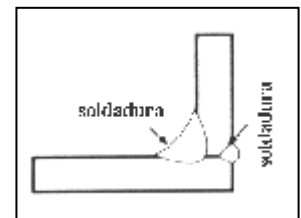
Esquina soldada desde ambos lados - pobre adentro, bueno afuera
